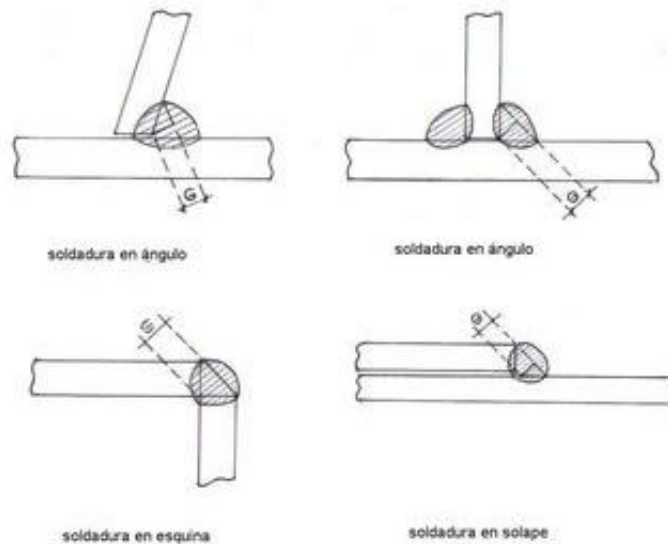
Cordón de soldadura en ángulo [41]
